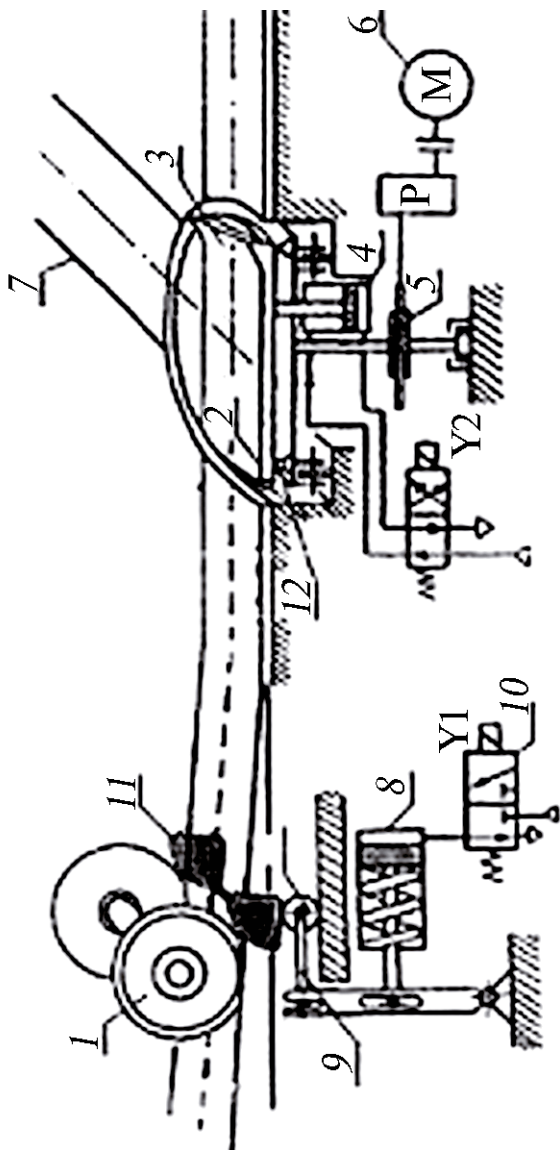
Устройство для поворота и передачи (сталкивания) колесных пар
